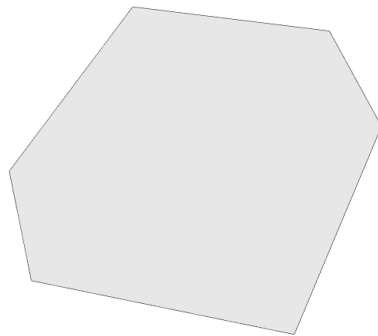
Probeta de control plana vista en planta (Elaboración propia)
